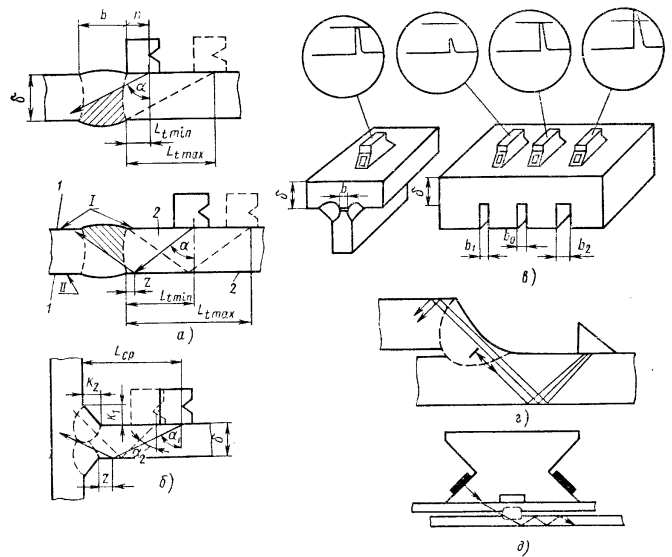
Схемы прозвучивания сварных соединений: I, II — поверхности соединения; 1, 2 — стороны соединения
